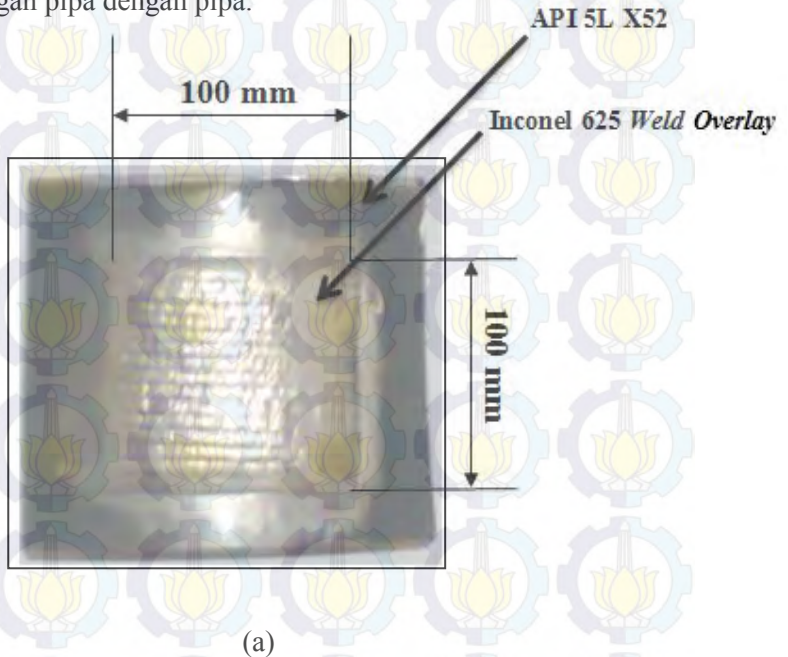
Skema Proses Pembuatan Pipa Inconel 625 *weld Overlay Cladding
